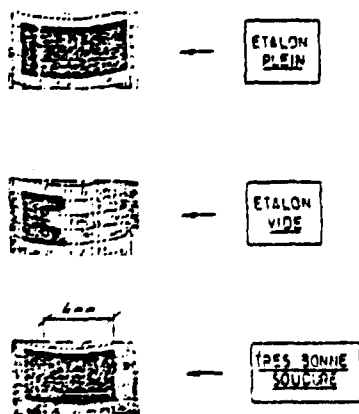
CONTRÔLE ULTRASONORE DES SOUDURES PAR MAGNETOSOUDEGE
